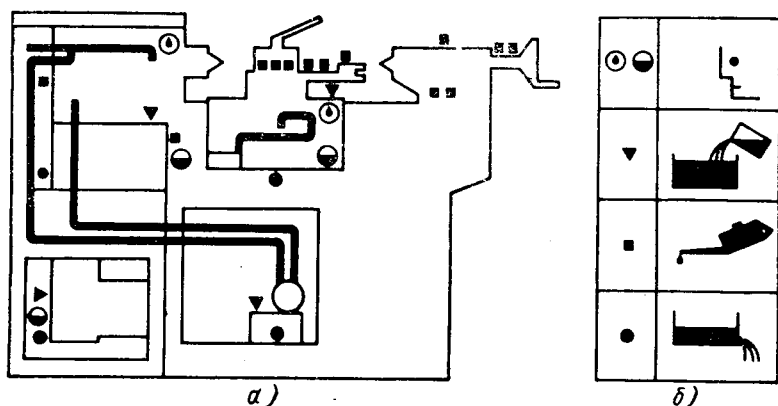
Схема смазки станка 1ИБ11П, выполненная с помощью символов:
